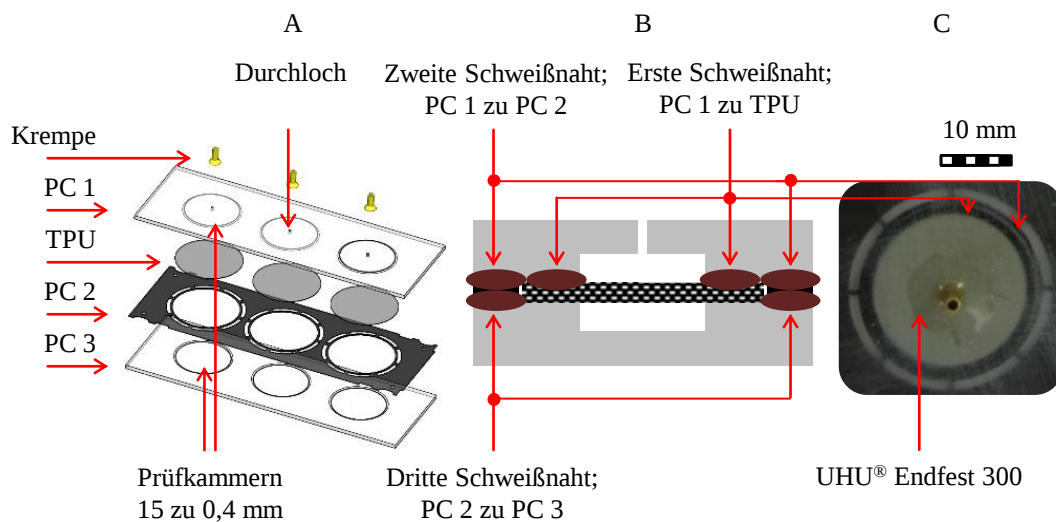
Prüfkörper für Druckprüfung PC zu PC Schweißung; A) CAD Dreilagenaufbau mit Materialien PC und TPU in einer Ebene; B) Schematische Darstellung Querschnitt durch Prüfkammer; C) Bild einer Prüfkammer vor der Druckprüfung; PC zu TPU: Verfahrensgeschwindigkeit 50 mm sec⁻¹, Wiederholfrequenz CW, Laserleistung 1600 mW, Anpressdruck 400 kPa_{rel}; PC zu PC: Verfahrensgeschwindigkeit 50 mm sec⁻¹, Wiederholfrequenz CW, Laserleistung 2170 mW, Anpressdruck 600 kPa_{rel}.
